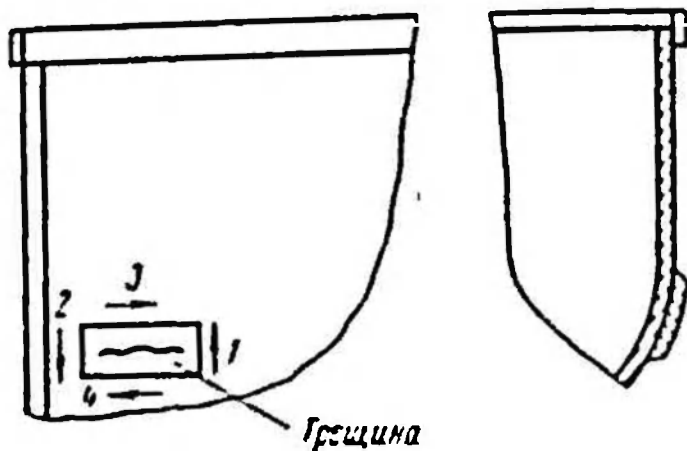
Очередность наложения швов и направление сварки трещин в кузове вагонетки
